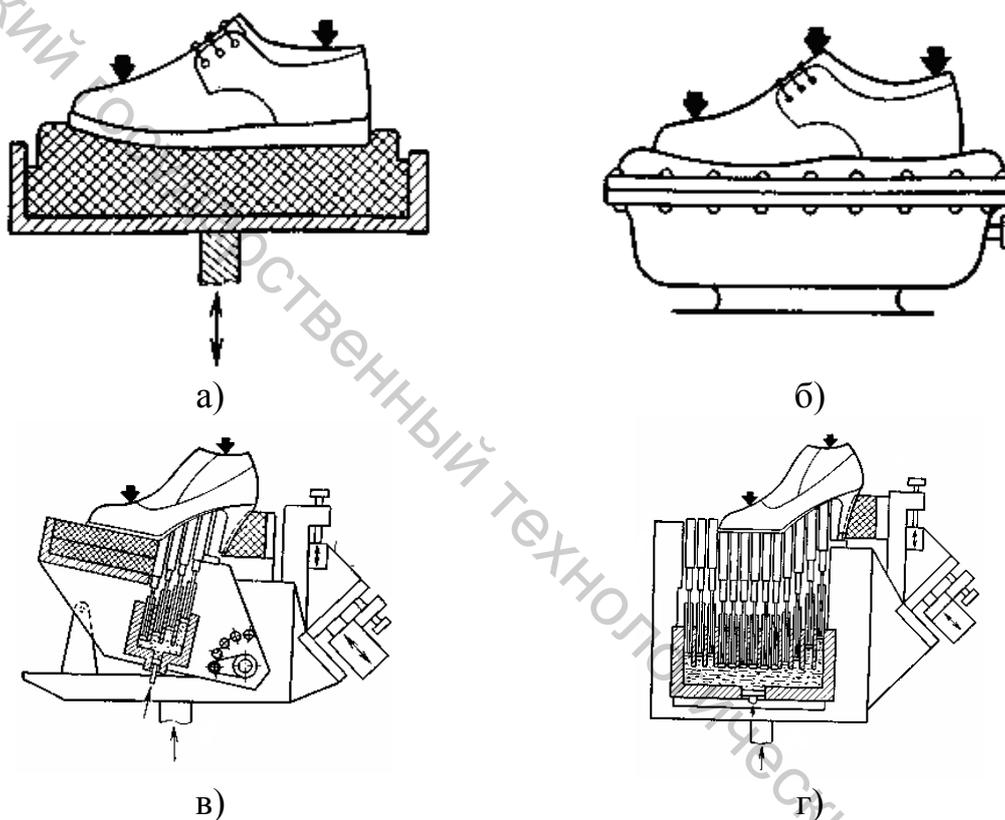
Конструкции пресс-подушек прессов для приклеивания подошв:
